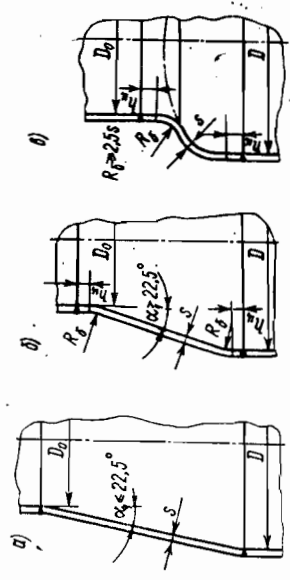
Конструкции переходов для стальных сварных аппаратов: а — конические без отбортовки; б — конический с отбортовками с обеих сторон; в — обратновогнутый
